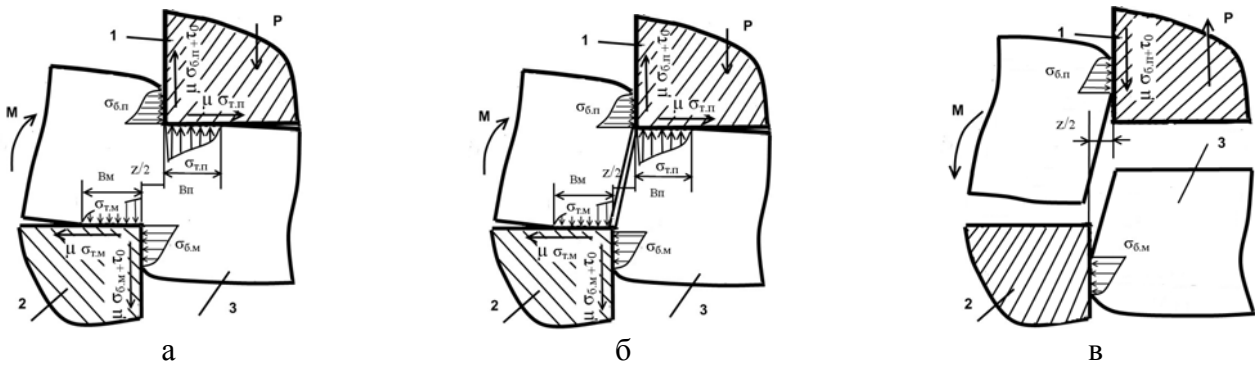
Эпюры нормальных и касательных напряжений на стадии разделения металла: а – пластического среза; б – проталкивания отделяемой части заготовки; в – обратного хода пуансона
